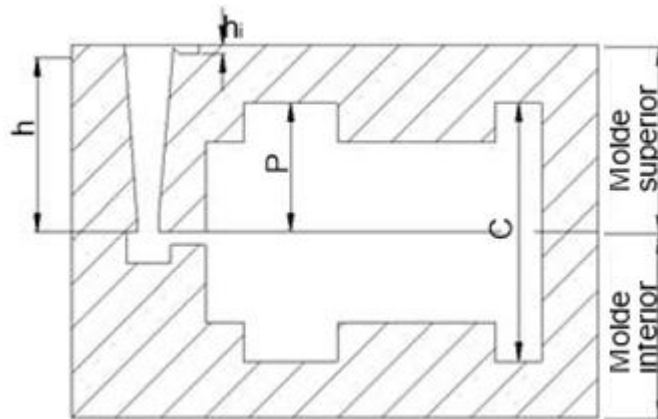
Vista lateral para el diseño de los componentes del molde.
